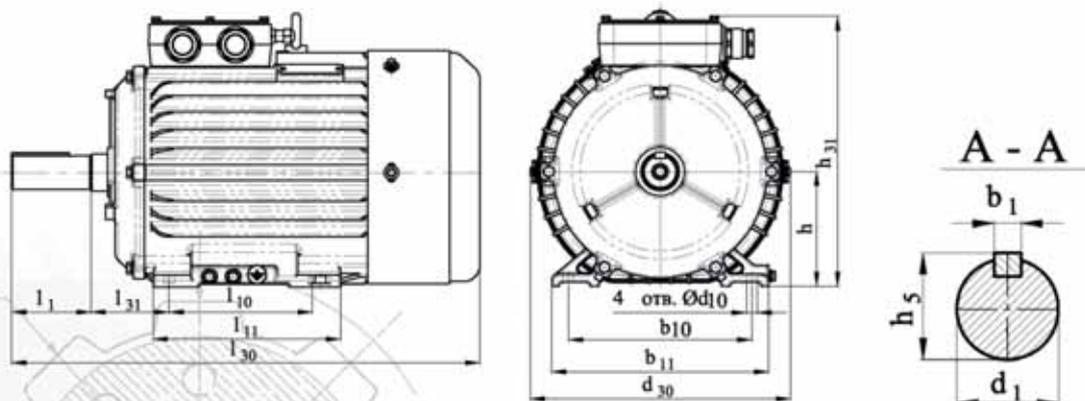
Габаритные и установочно-присоединительные размеры двигателей для привода станков-качалок
